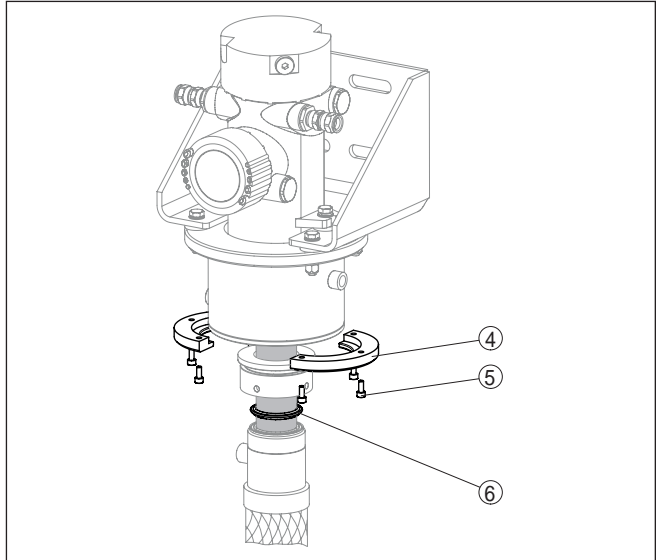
Montage-Kit - Szintillator-Kühlschlauch - oben
